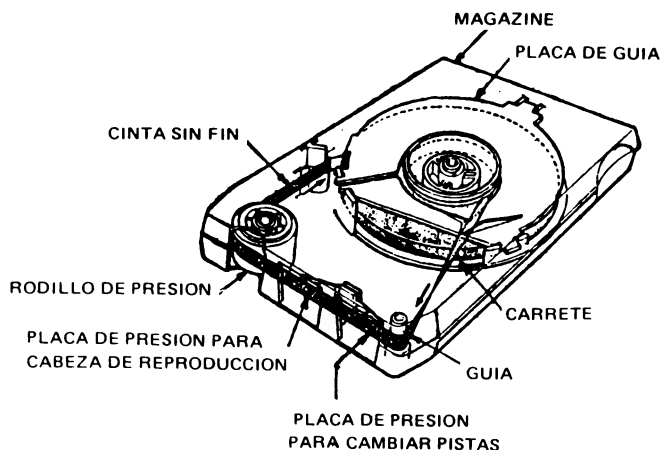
Vista interior de una caja portacinta tipo magazine para apreciar su construcción interna.
